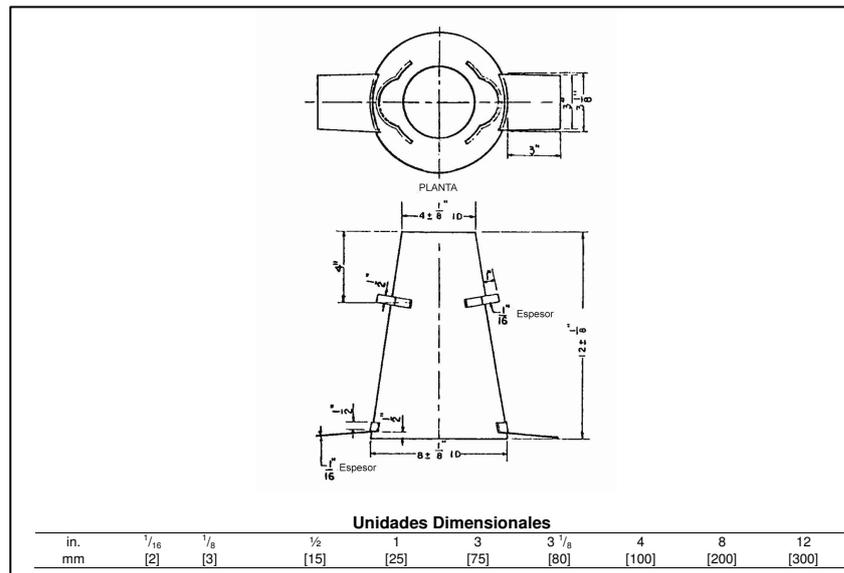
Dimensionamiento del molde para ensayo ASTM C143
